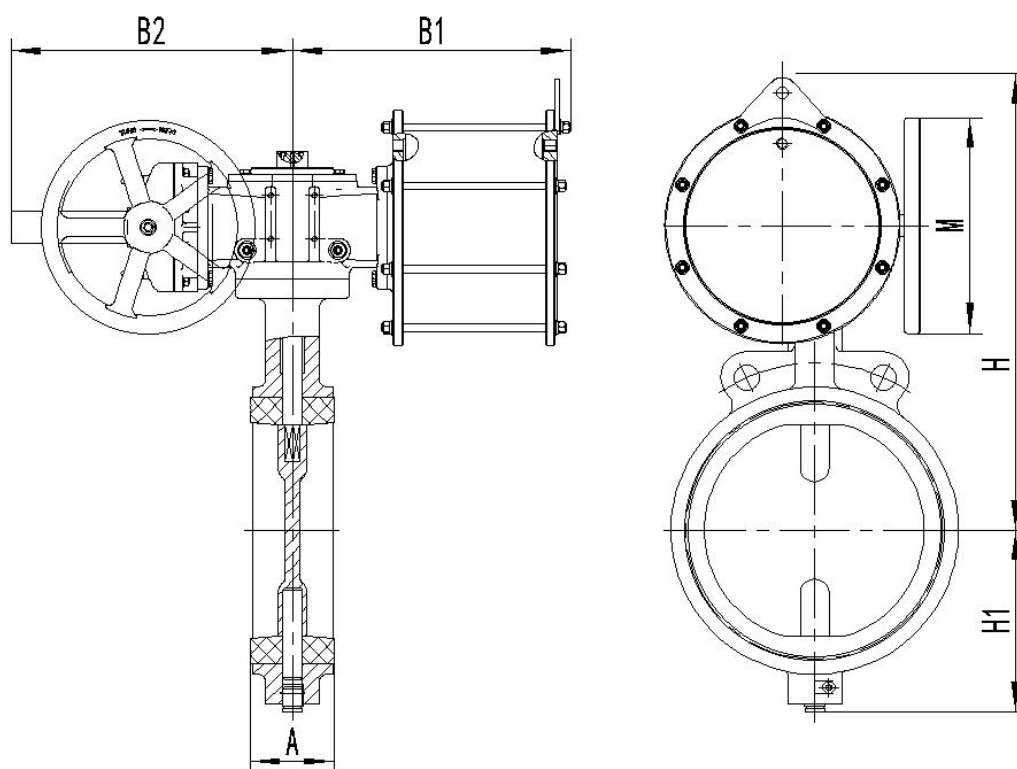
配 HCW27D003~HCW35D004 带伞齿手轮外形尺寸图
